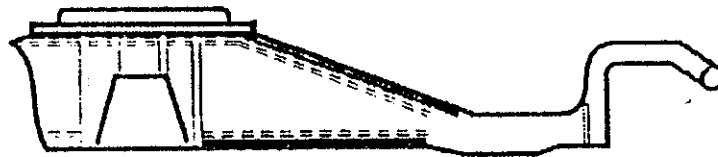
Контроль сварных соединений боковой стенки с верхней и нижней пластинами
